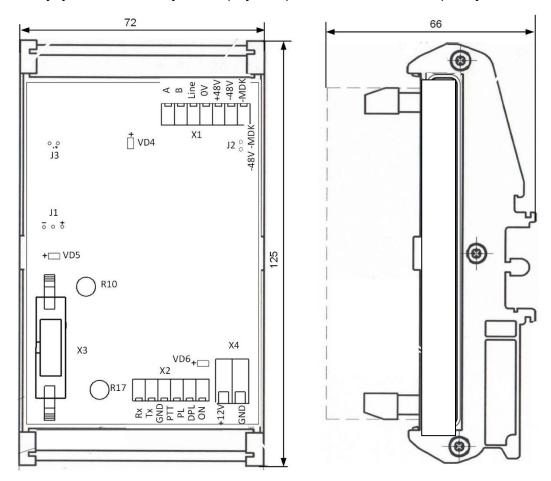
Внешний вид и габаритные размеры шлюза
